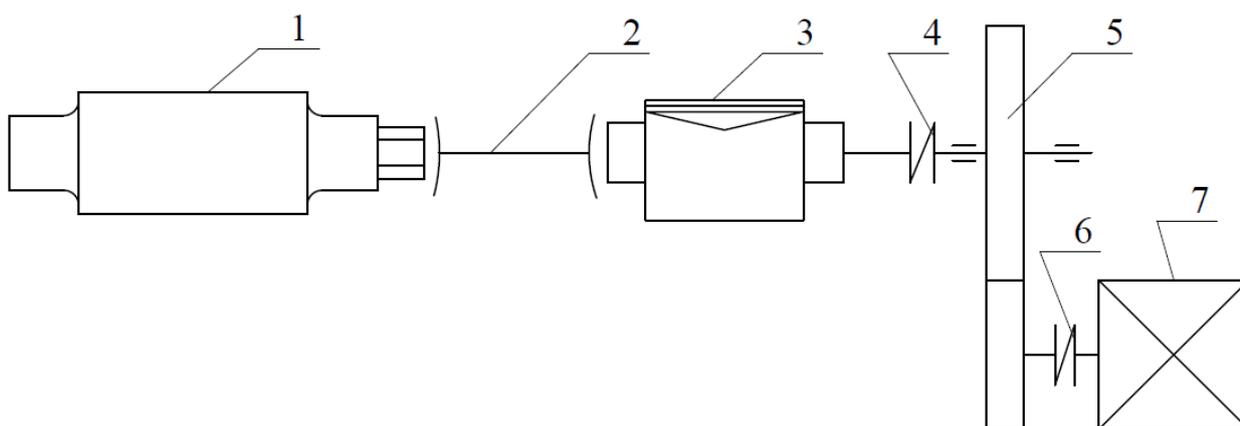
Схема главной линии прокатного стана: 1-рабочая клетка; 2-соединительные шпиндели; 3-шестеренная клетка; 4-коренная муфта; 5-редуктор; 6-моторная муфта; 7-двигатель.
